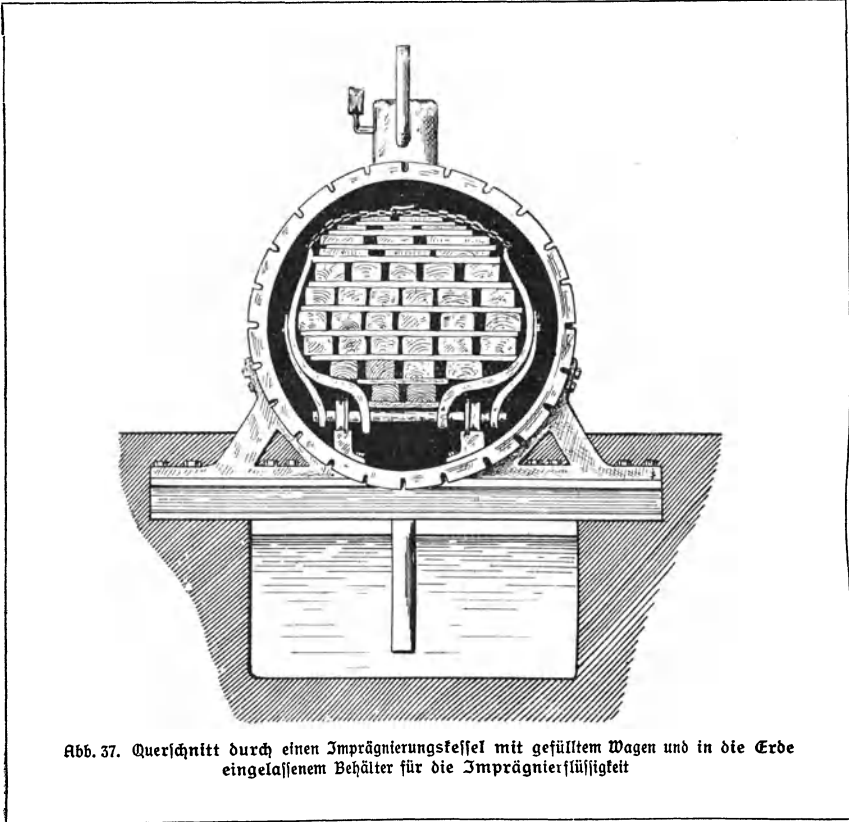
Querschnitt durch einen Imprägnierungskessel mit gefülltem Wagen und in die Erde eingelassenem Behälter für die Imprägnierflüssigkeit
